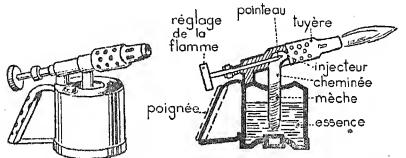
Lampe à souder. A gauche, vue d'ensemble. A droile, coupe montrant l'intérieur de la lampe.
